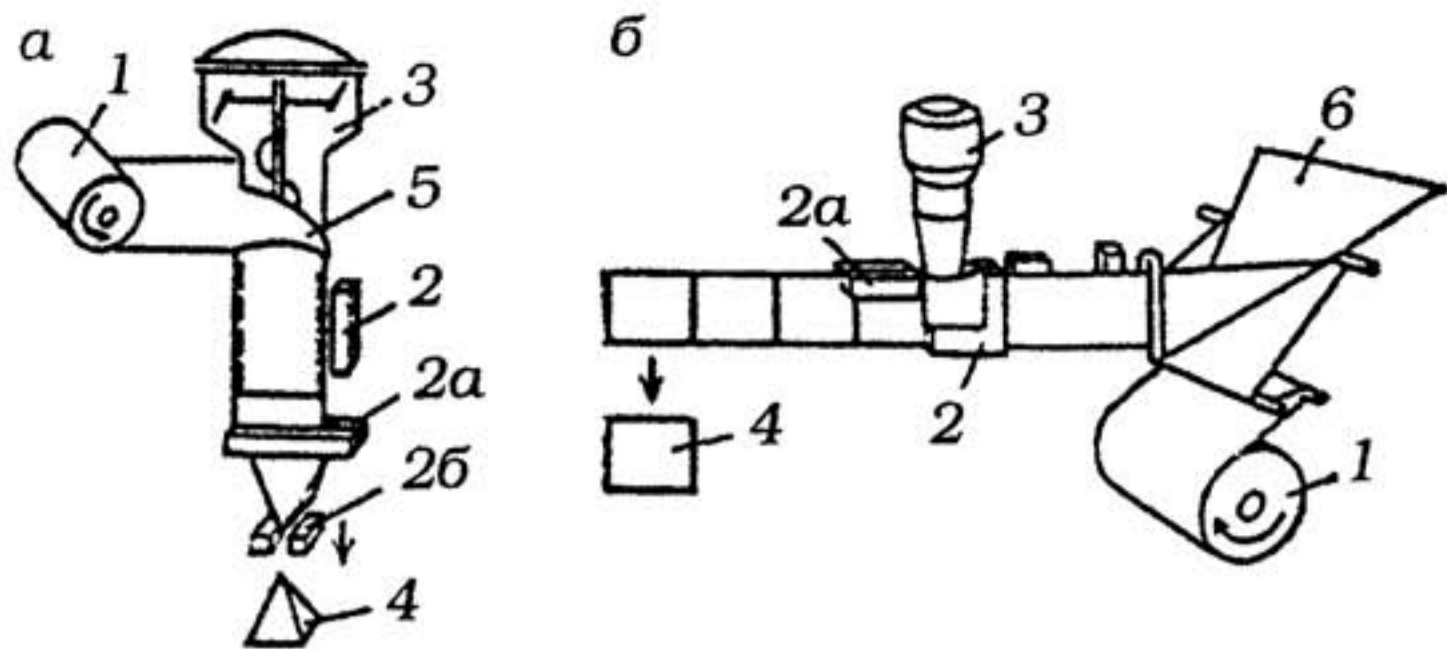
Схема вертикального способа изготовления мягкой тары с формующим воротником (а) и с формующим треугольником (б): 1 — рулон пленки; 2 — сварочные элементы; 3 — бункер с дозатором; 4 — упаковка; 5 — формующий воротник; 6 — формующий треугольник
